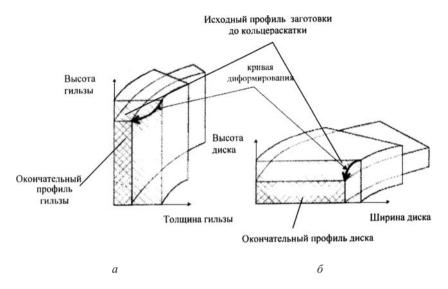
Кривые деформирования для гильзы и диска [3]: a – детали типа гильзы; δ – детали типа диска
